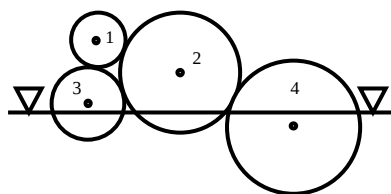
Относительное расположение зубчатых колес и масляной ванны коробки передач:
